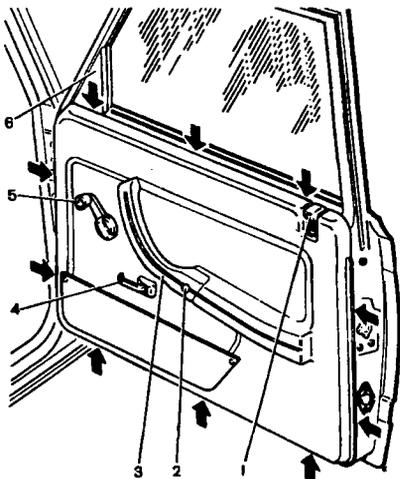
Вид внутренней стороны двери: 1 - кнопка блокировки замка; 2 - декоративная заглушка; 3 - ручка подлокотника; 4 - внутренняя ручка привода замка; 5 - ручка стеклоподъемника; 6 - заглушка окна. Стрелками показано расположение держателей обивки двери
